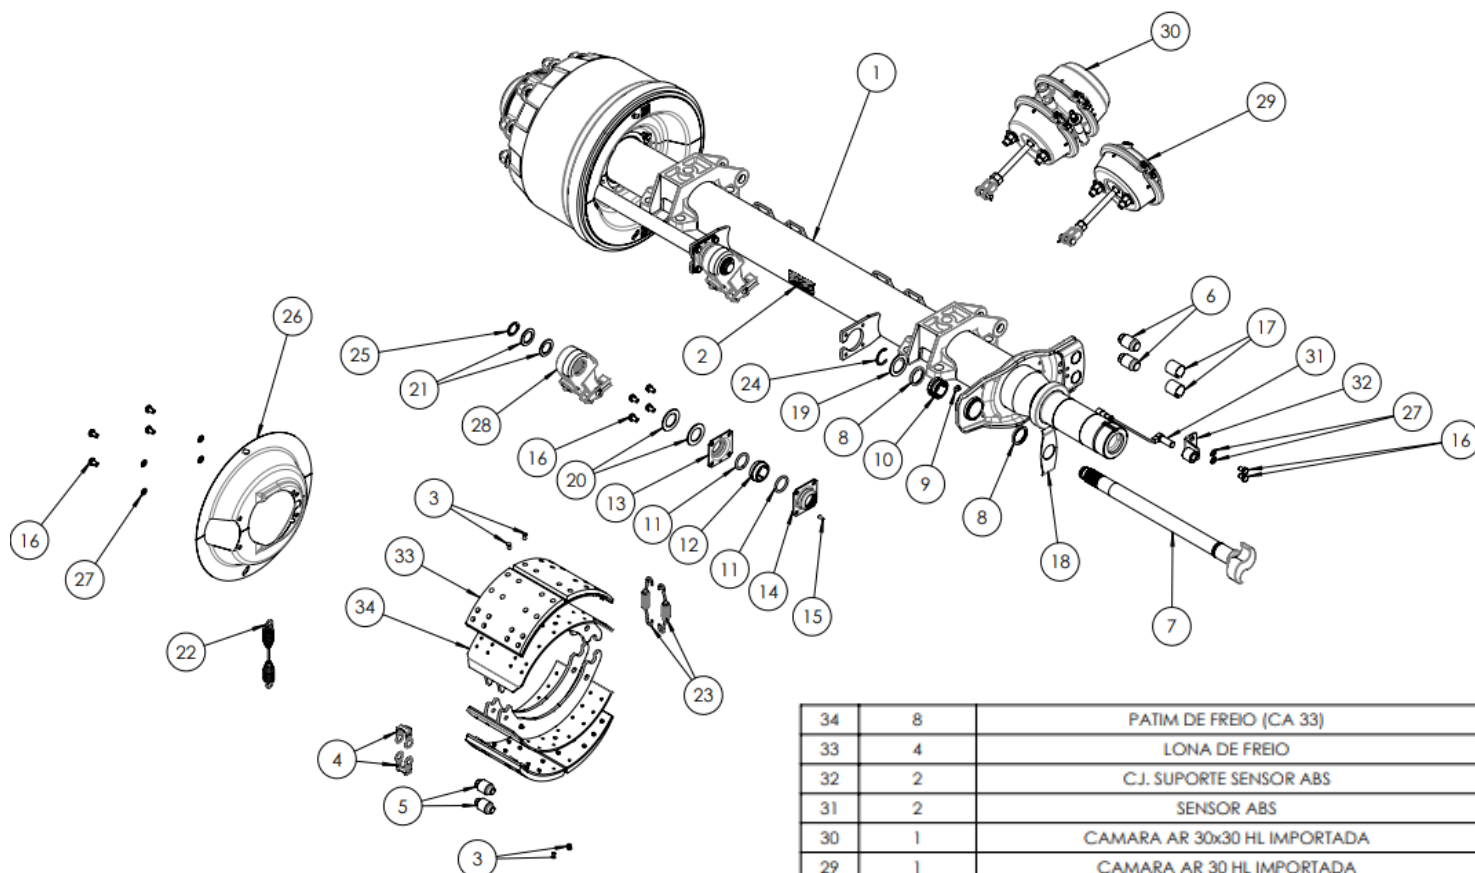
VISTA EXPLODIDA COMPONENTE DO FREIO.
